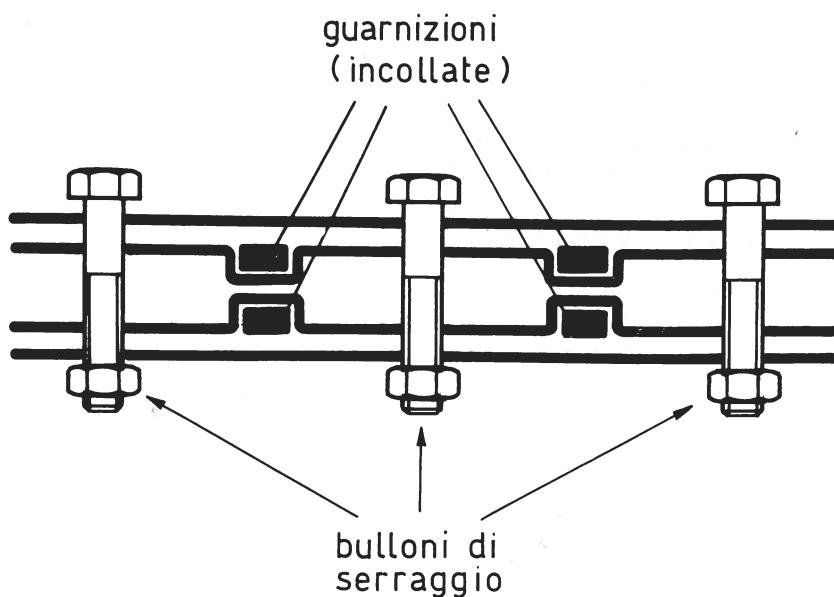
Assemblaggio per le prove di tensocorrosione sotto le guarnizioni.
